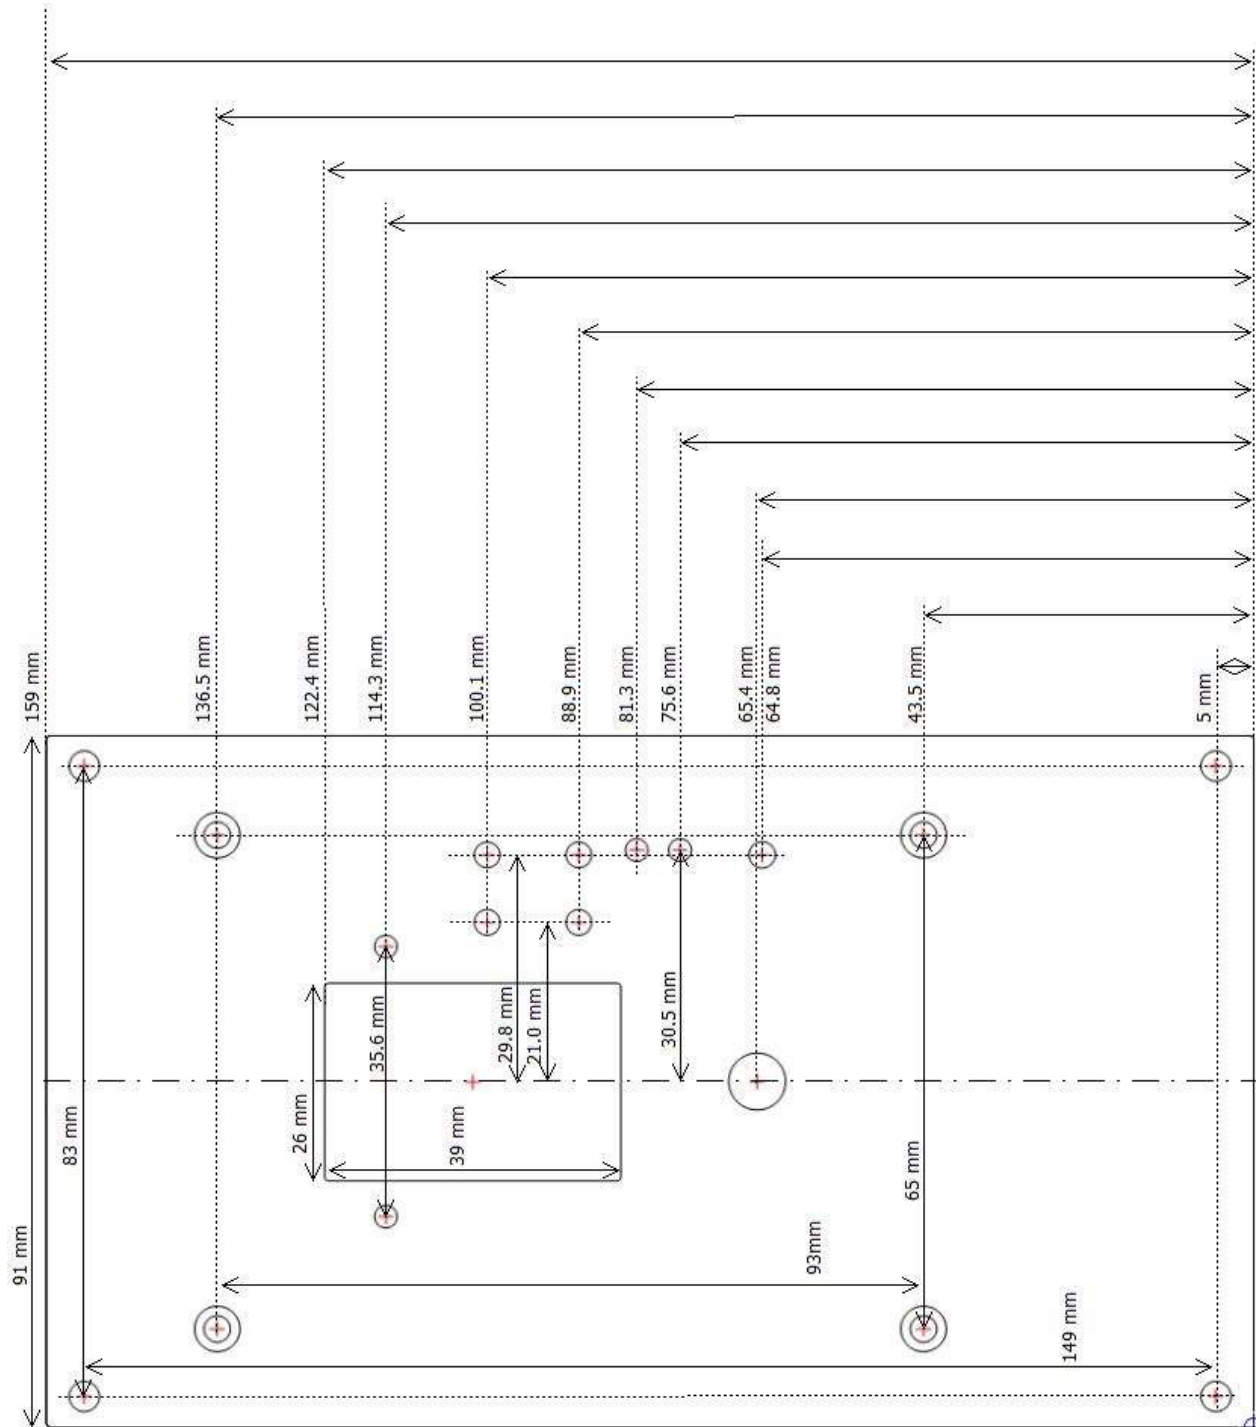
Maßzeichnung Frontplatte für Teko 103 Gehäuse
